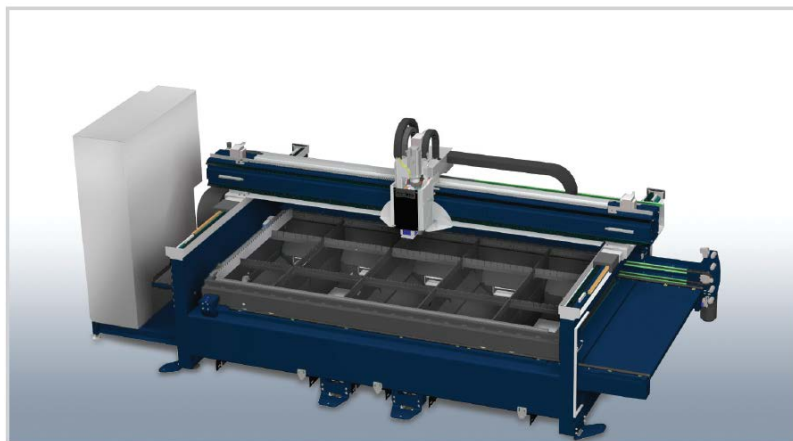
Máquina de corte laser ADIRA - Blue Laser com 3 eixos (ADIRA S.A., 2016)
